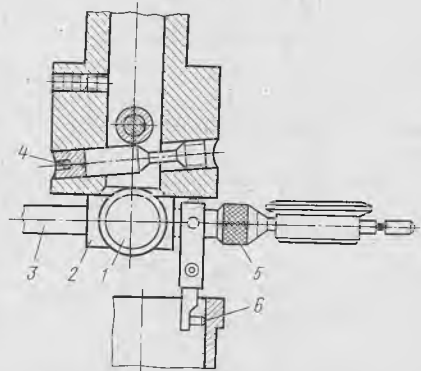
Резцовая головка станка 2А78Н с приспособлениями для центрирования гильзы: 1 — винт; 2 — колодка; 3 — рычаг; 4 — шариковая оправка; 5 — гайка; 6 — упор рычага
